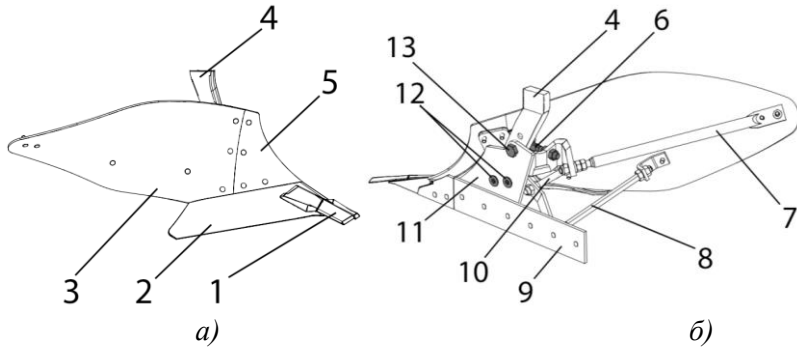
Корпус плуга: а – вид спереду; б – вид ззаду;
